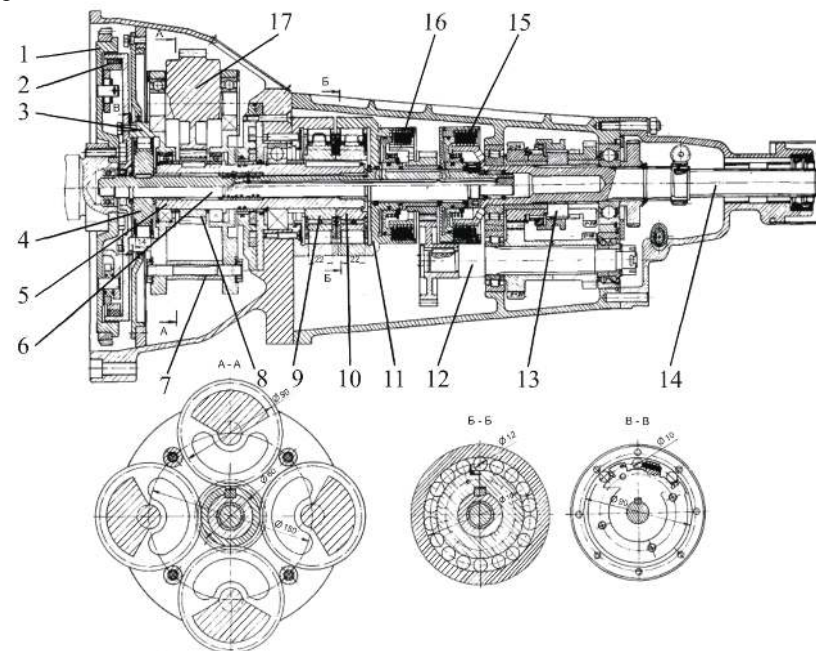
Конструкция опытной автоматической коробки передач автомобиля ИЖ-2126
